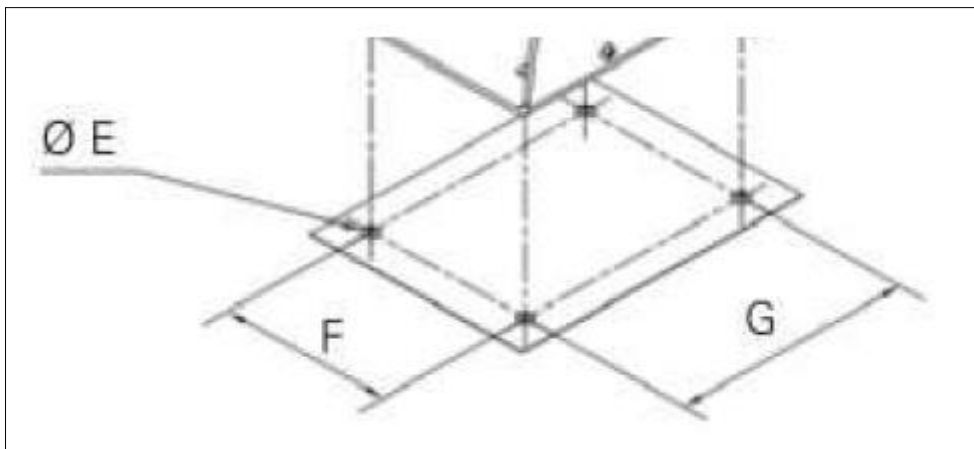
44 Dimensions de la ubicació dels forats de subjecció del motor
